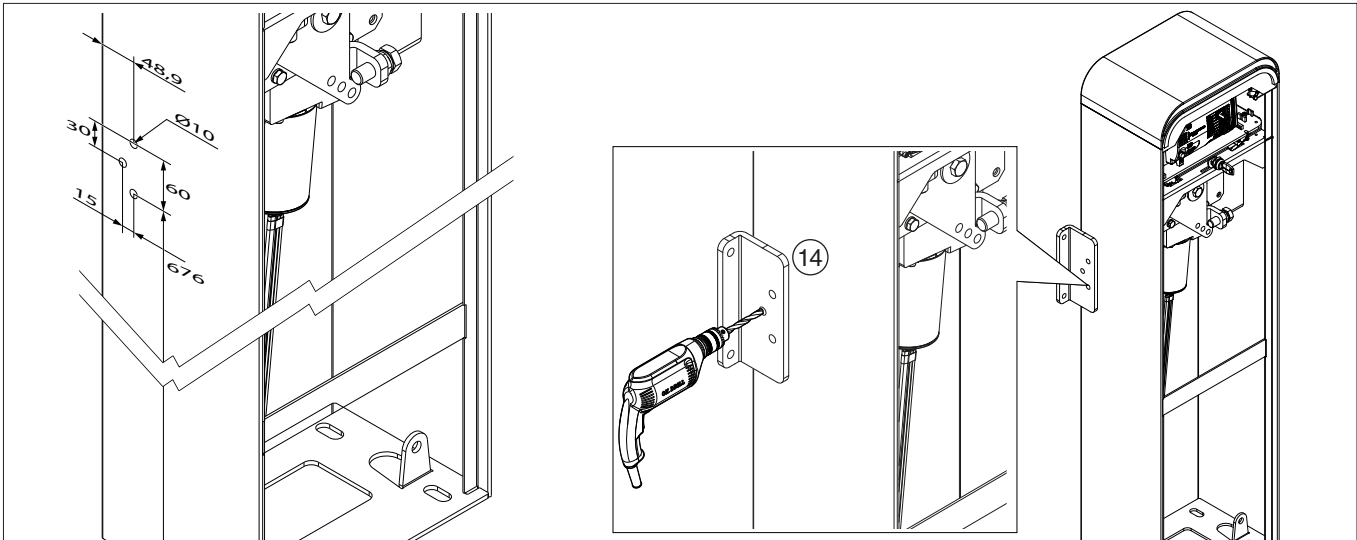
INSTALLAZIONE PIASTRINA PIEGATA / BENT PLATE INSTALLATION
